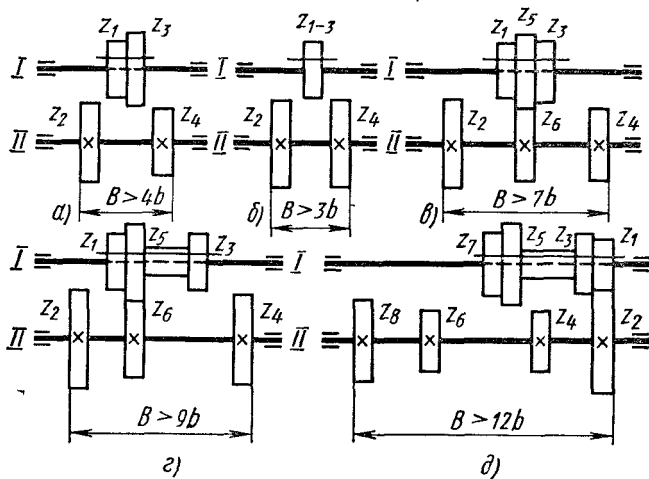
Множительные механизмы с многовенцовыми блоками зубчатых колес
